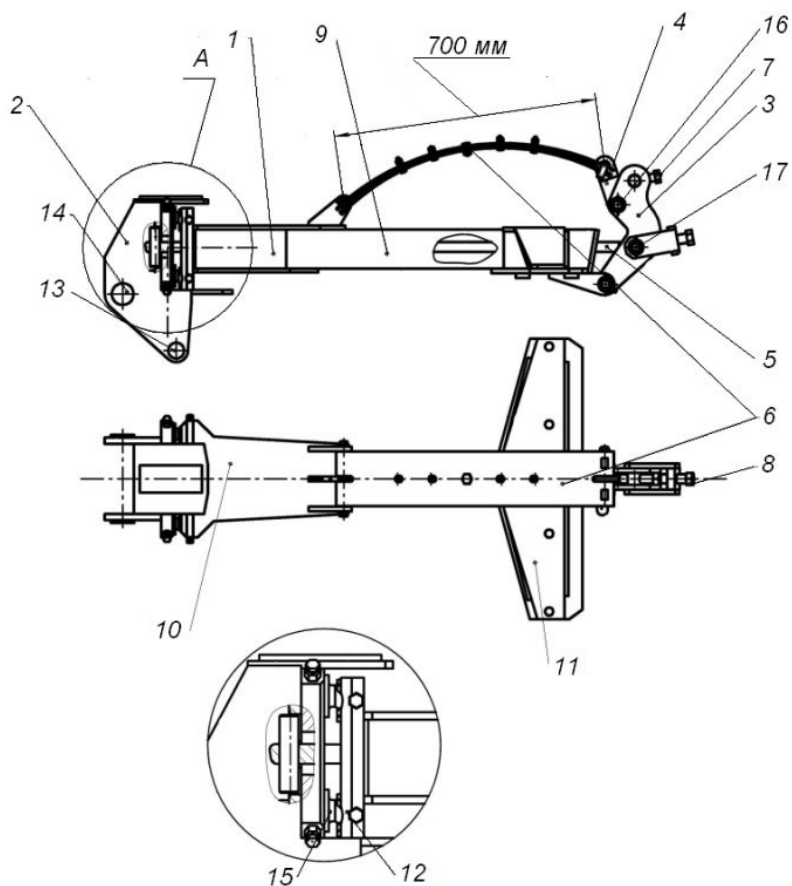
Предохранитель: 1 – грядиль; 2, 10, 11 – кронштейны; 3, 4 – рычаги; 5 – тяга; 6 – пластинчатая пружина; 7, 8 – болты регулировочные; 9 – труба; 12 – упоры; 13, 14 – болты; 15 – цапфы; 16, 17 – оси
